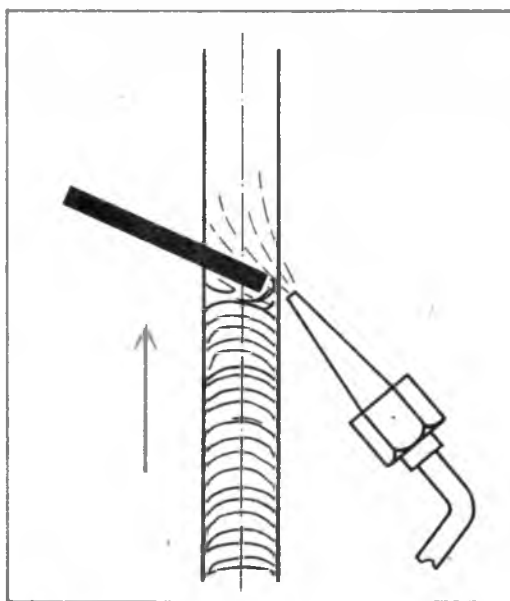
Сварка снизу вверх (простая сварка)
